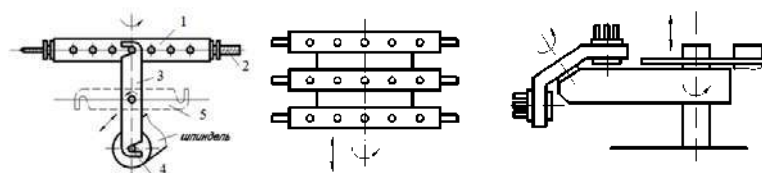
Промежуточный транспортный манипулятор с помощью двухзахватной руки
